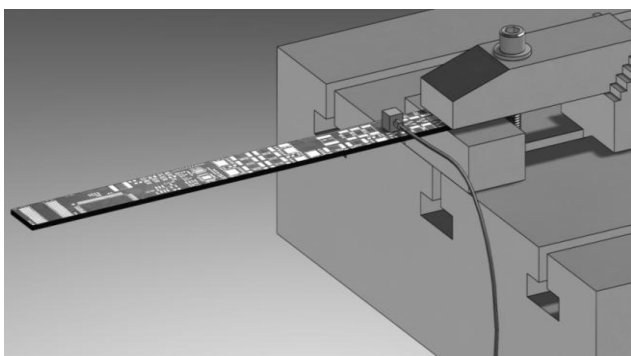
Внешний вид образца для испытаний с приклеенным акселерометром
